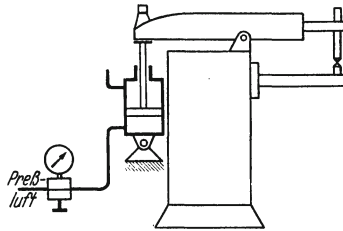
Erzeugen durch Preßluft oder Drucköl, Regeln durch den Druck des Druckmittels.
